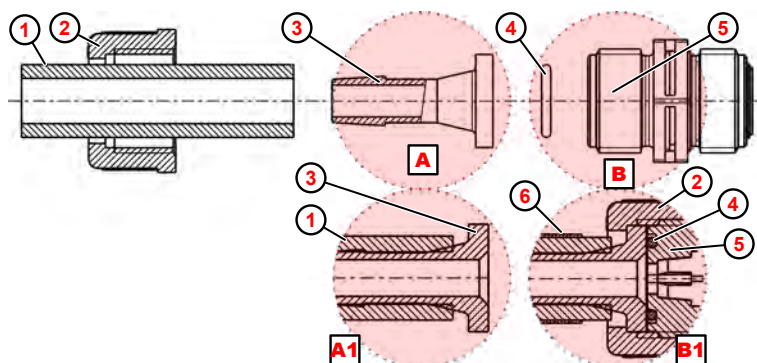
Collegamento tubi rigidi e tubi flessibili con raccordo filettato di fissaggio e fascetta tubo flessibile
